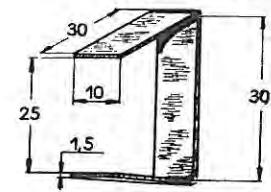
Bügel für die Halterung der Lichtmaschinenkolben-MR-4158-30
